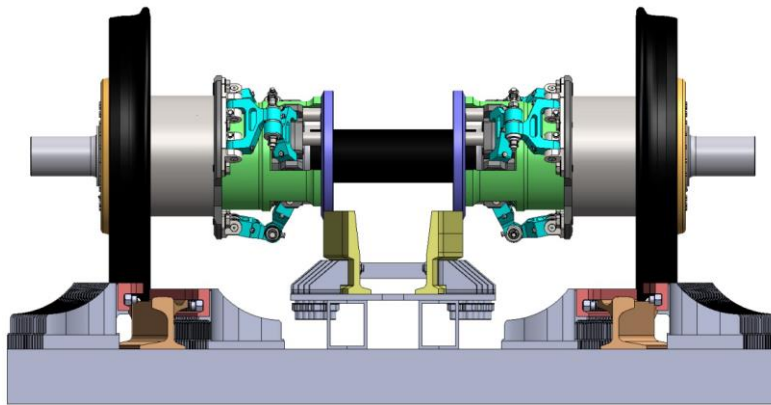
Eje EAVM en posición de ancho estándar 1668 mm
